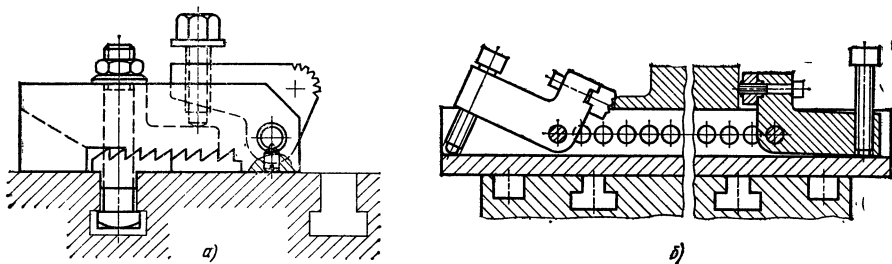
Быстросменляемые ЗМ для закрепления заготовок сбоку с перестановкой прихвата:
